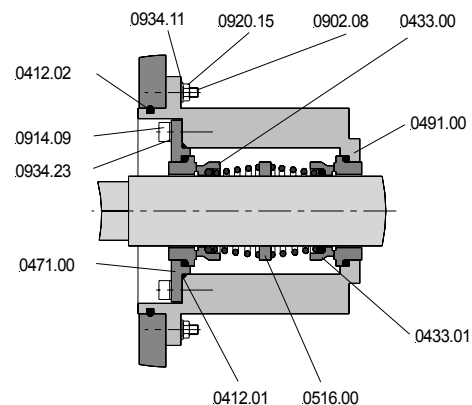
Doppelte Gleitringdichtung back-to-back (D)
